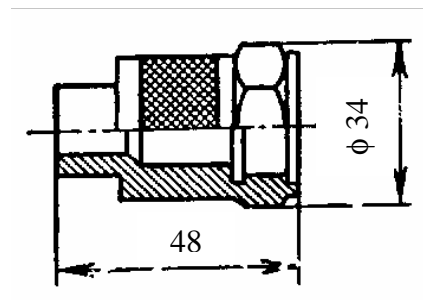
Деталь-корпус свечи двигателя, обрабатываемой на автомате
